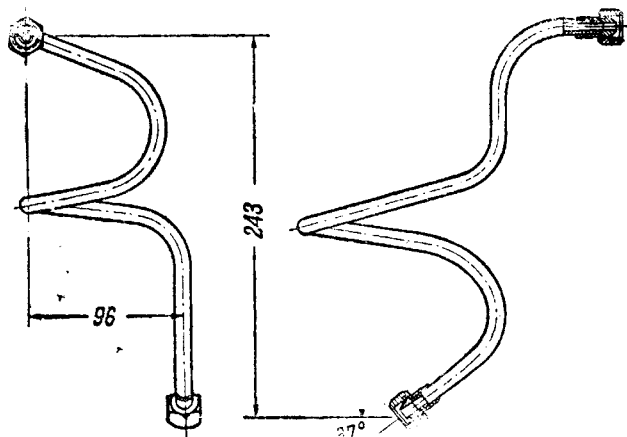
Изменённый изгиб трубки рубашки блока цилиндров двигателя АЕС А190
